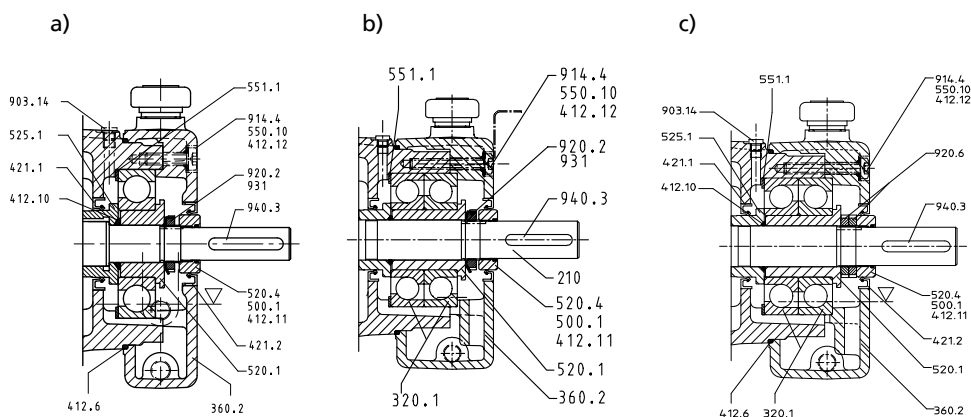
Масляная смазка, радиальное кольцевое уплотнение: а) типоразмер 32 и б) типоразмер 50-65 и с) типоразмер 100-150
